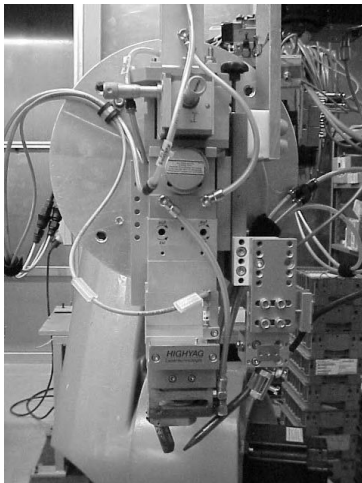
Aluminium-Schweißkopf für den Nd:YAG-Laser
